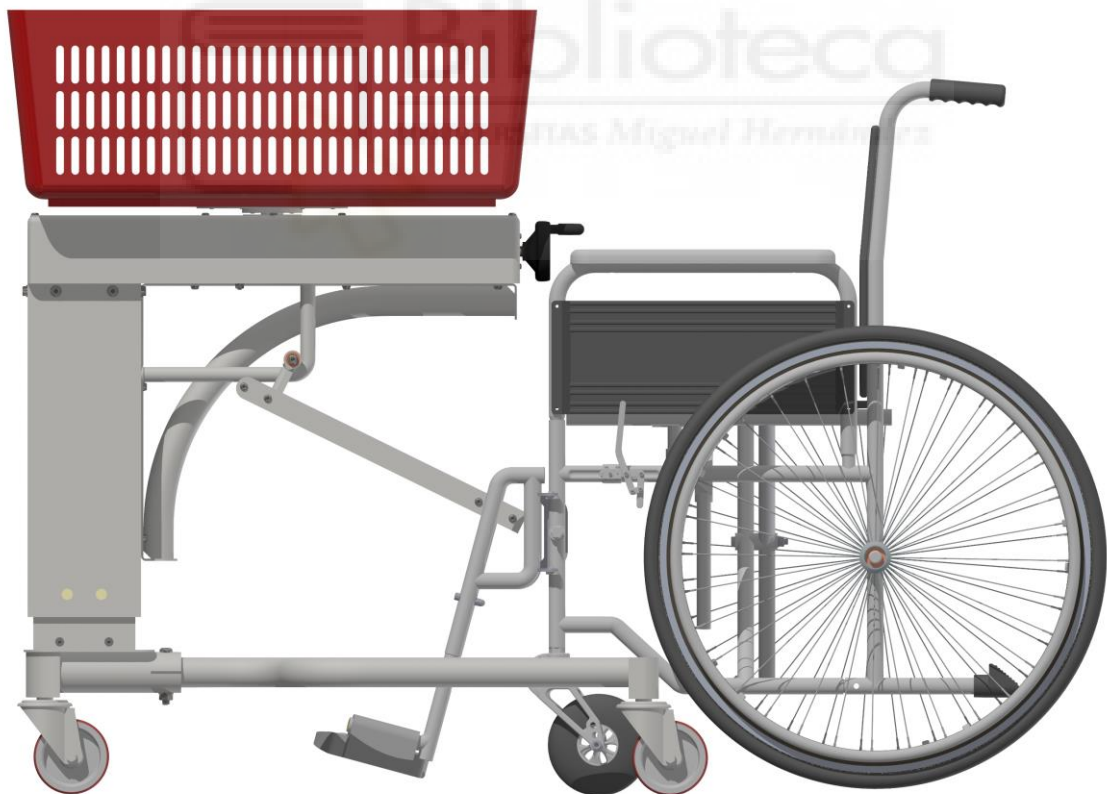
Conjunto carrito-silla de ruedas. Vista de perfil.
